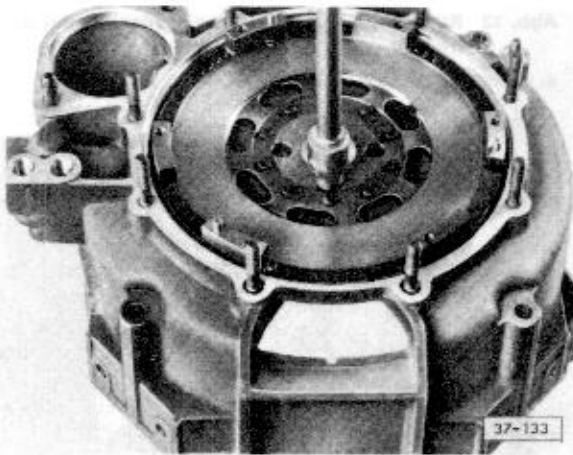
Schrauben für Freilaufstütze herausschrauben
